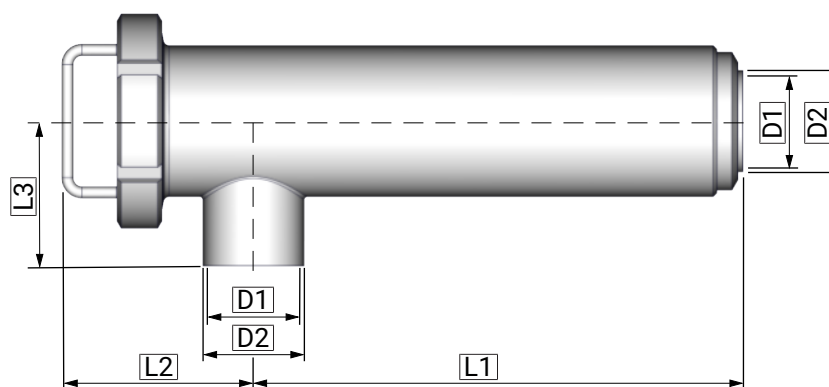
Ejemplo de dibujo con conexión soldada
